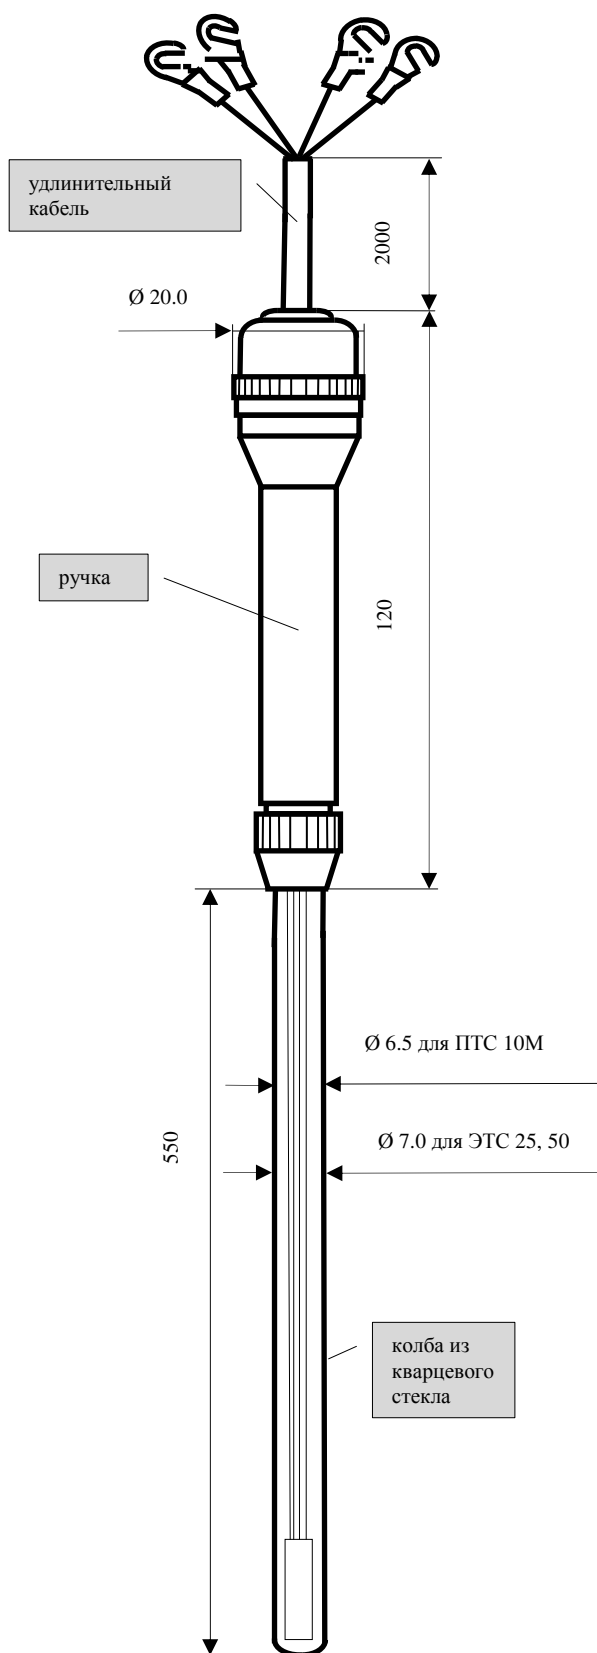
Габаритные и присоединительные размеры ПТС-10М и ЭТС-25
